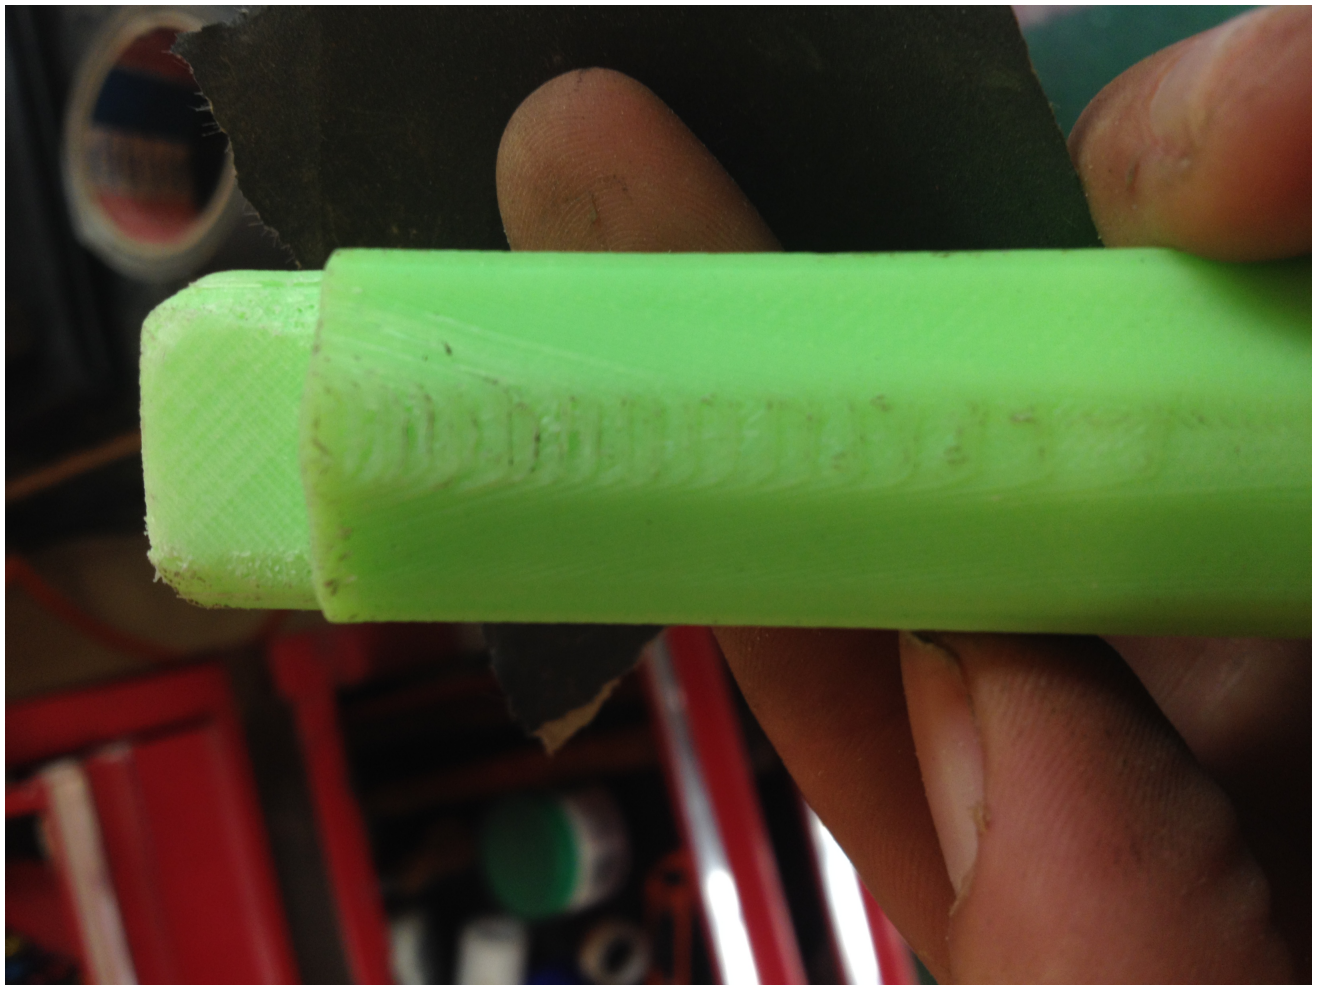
Ensamblaje. Proceso de retirada de material del molde interior para que pueda ser instalado. (Fuente: Propia)
